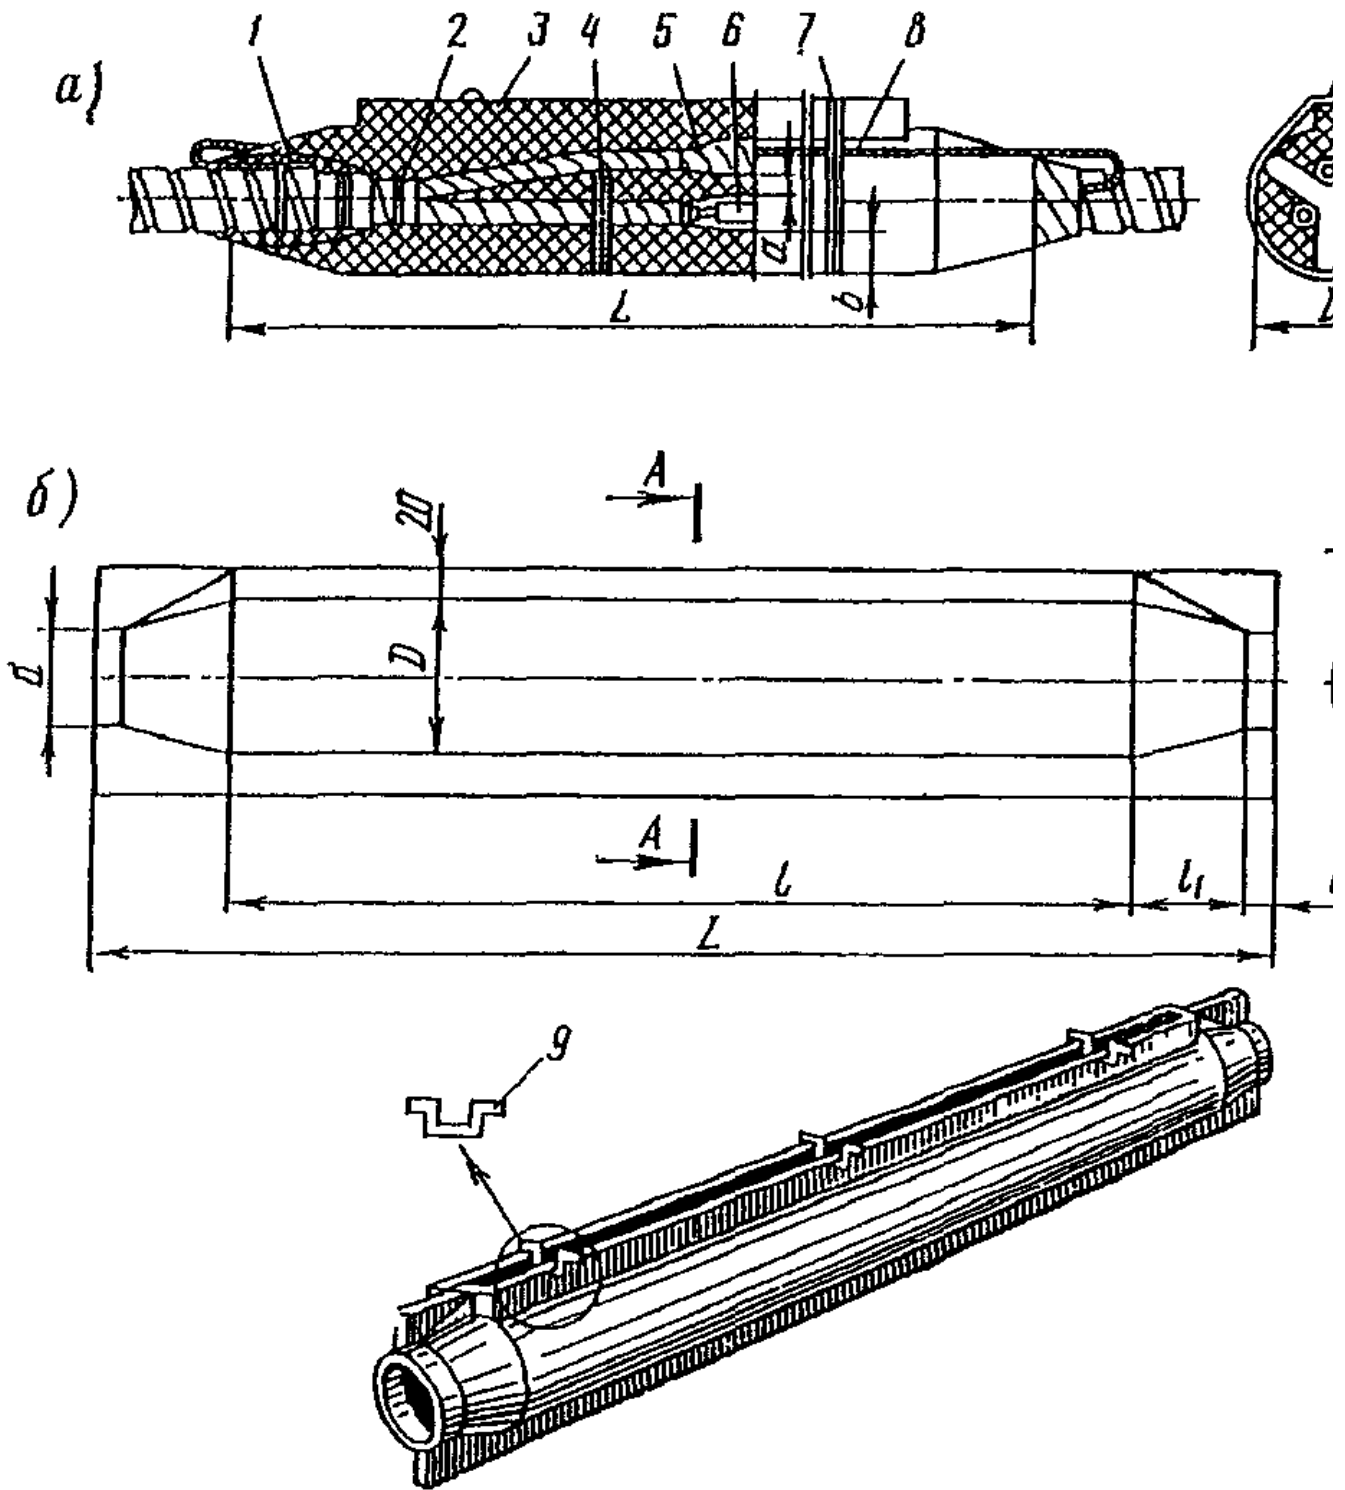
Соединительная муфта типа СЭ и съемная форма для ее монтажа: а - муфта; б - съемная форма из пластмассы или листовой стали; 1 - герметизирующая подмотка; 2 - бандаж из суровых ниток; 3 - корпус муфты; 4 - распорка; 5 - подмотка жилы; 6 - соединение жил; 7 - проволочный бандаж; 8 - провод заземления; 9 - скоба
